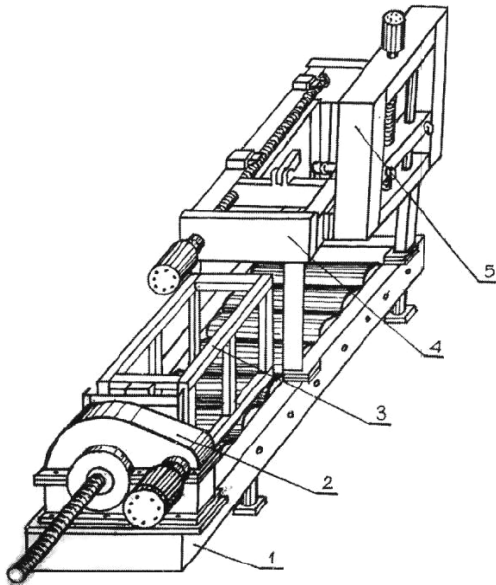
Принципова схема автоматизованого механізму подачі смуги: 1 – транспортер; 2 – привод переміщення касети; 3 – касета; 4 – механізм подачі заготовки; 5 – механізм підйому заготовки
